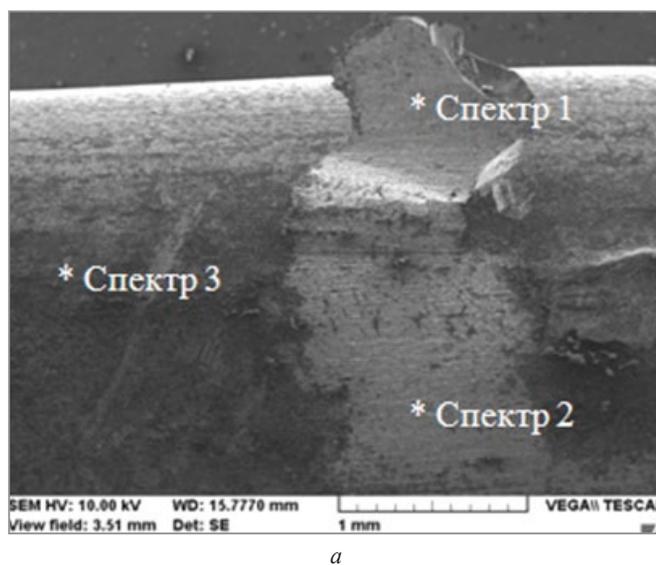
Образец катанки: *a* – внешний вид поверхности;
